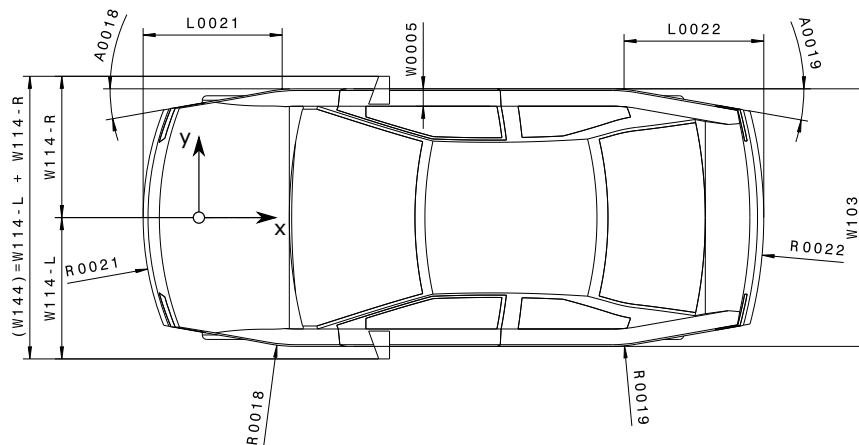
Hauptmaße Exterieur (Draufsicht)
